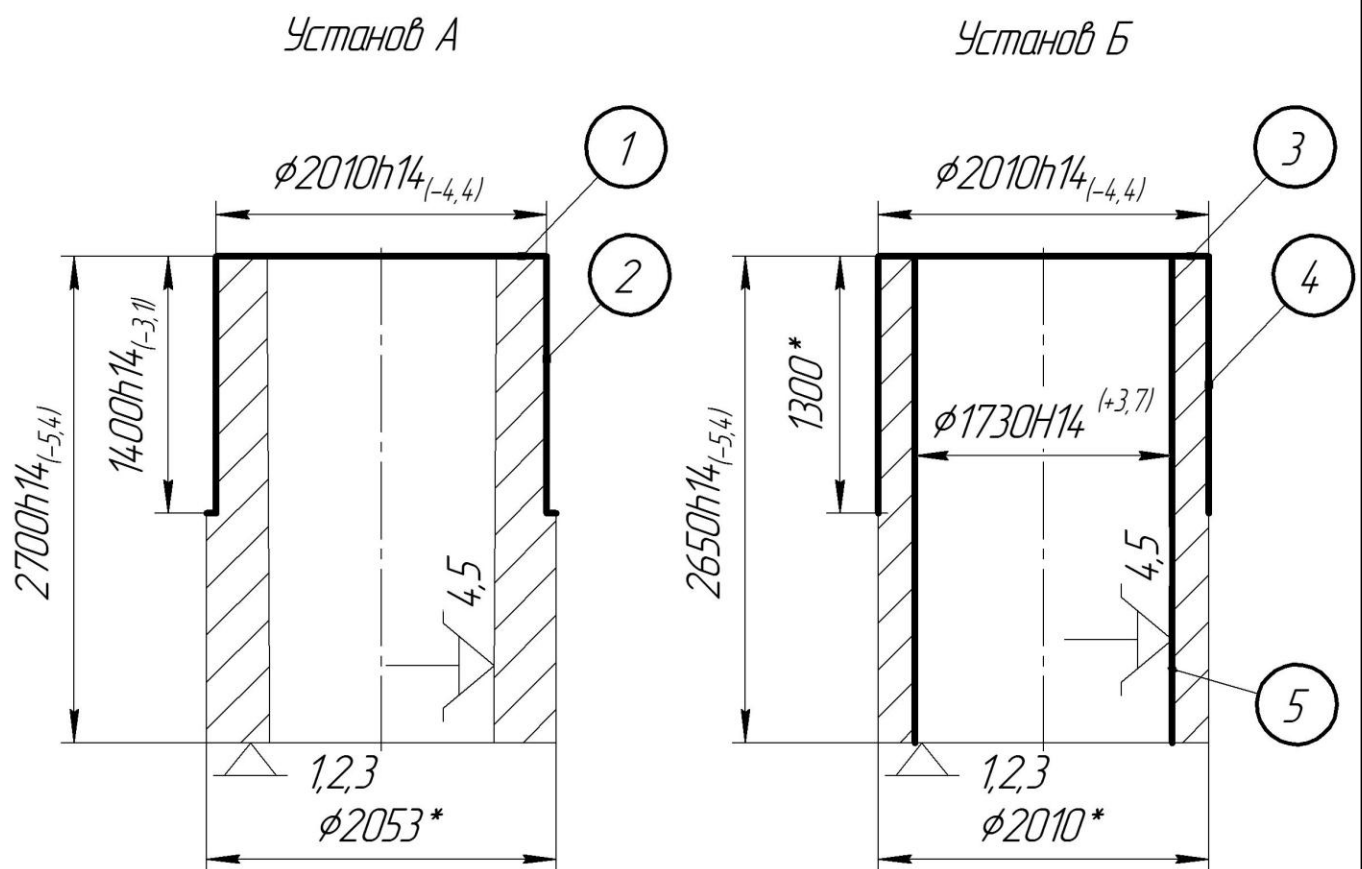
Схема базування заготовки на токарній з ЧПК операції (другий варіант)
